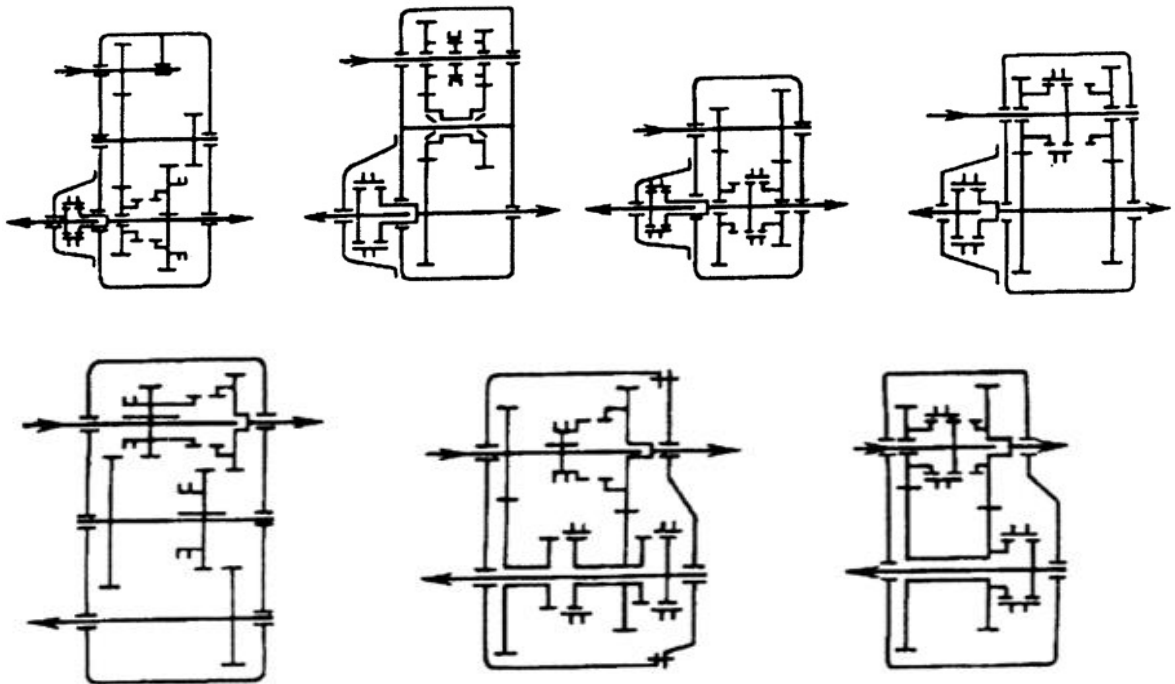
Схемы двухступенчатых раздаточных коробок с заблокированным приводом и соосным (сверху) и несоосными (снизу) ведомыми валами
